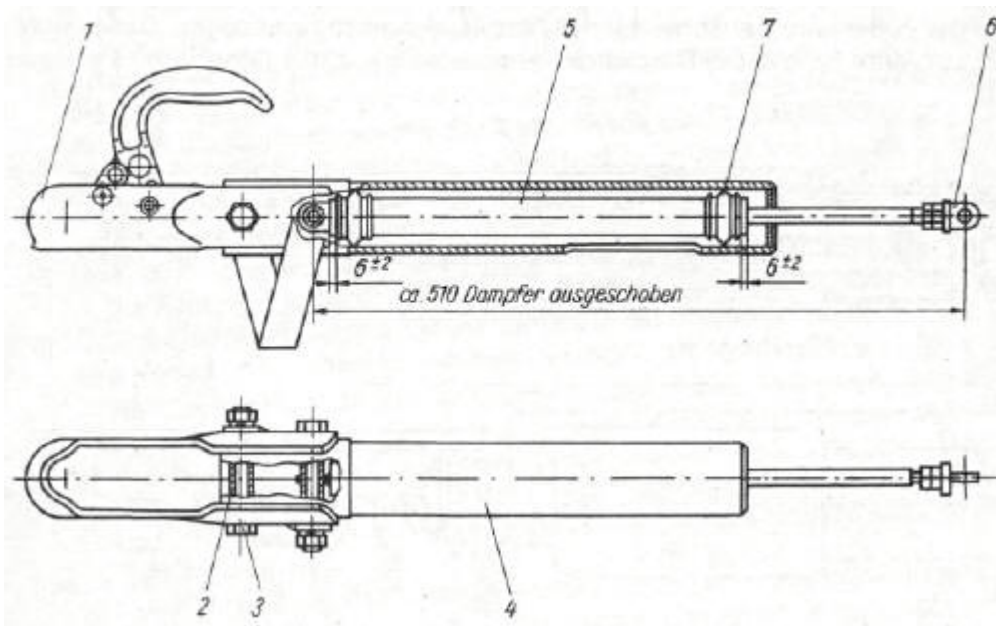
Auflaufkopf der mechanischen Auflaufbremse
